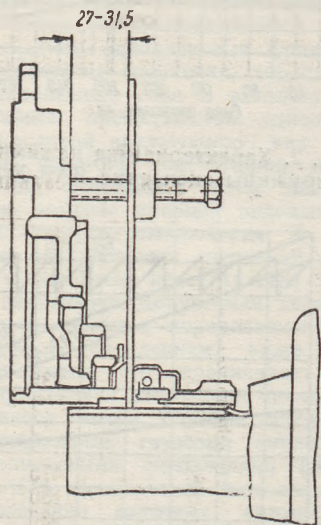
Эскиз приспособления для замера контрольного размера А.
